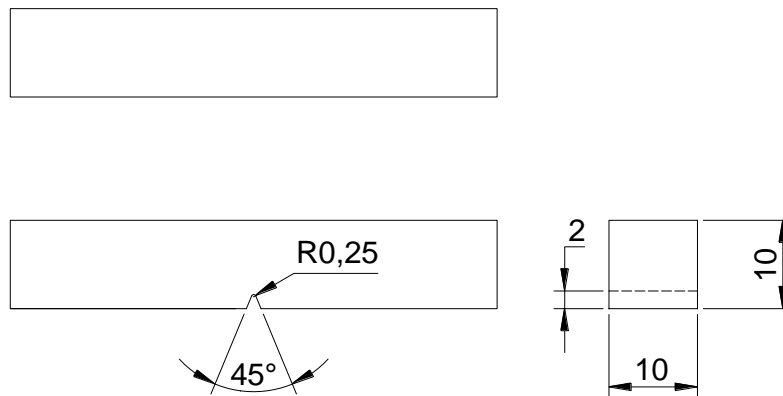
Probeta para ensayo de impacto bajo norma ASTM E23-02A.
